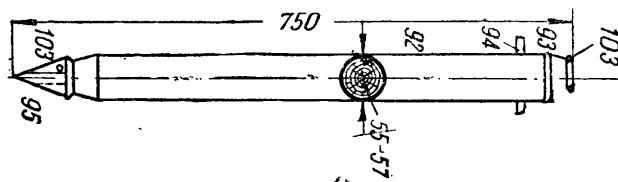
Кол деревянный: 92 — древко кола; 93 — кольцо; 94 — шпилька; 95 — башмак; 103 — гвоздь
